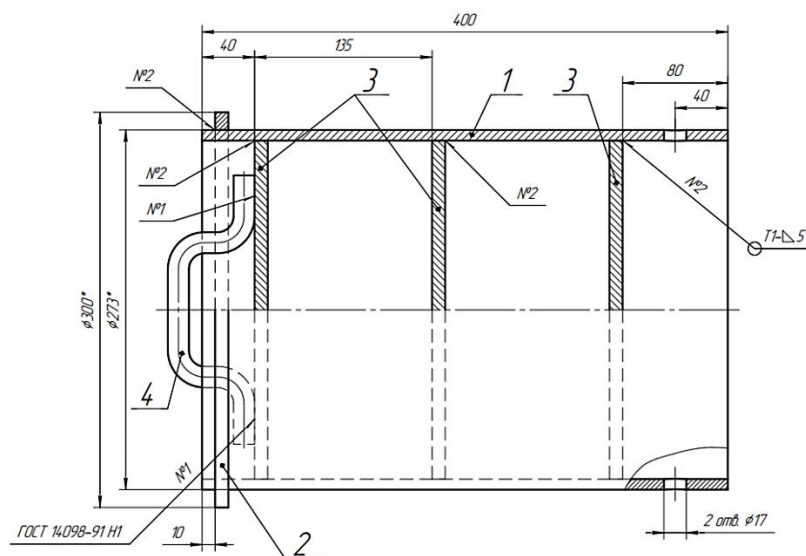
Палец: 1 – труба; 2 – ребро упорное; 3 – ребро силовое
